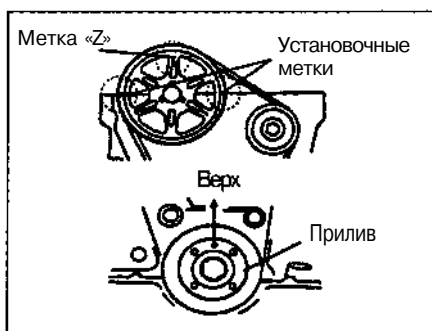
, б. Метки установки зажигания на звездочках коленчатого и распределительного валов - двигатель 1.5 литра с двумя распределительными валами
